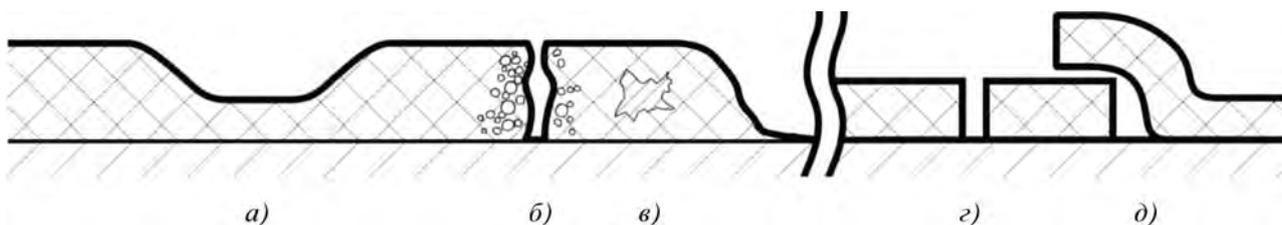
Схематическое изображение дефектов покрытия: а – недопустимое утонение; б – сквозная пора или трещина; в – металлическое включение; г – отсутствие покрытия (механическое повреждение); д – сквозное отверстие в области нахлеста листов покрытия
